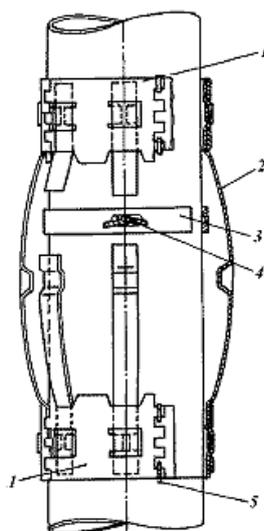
Передвижной центратор для установки на забойный двигатель
